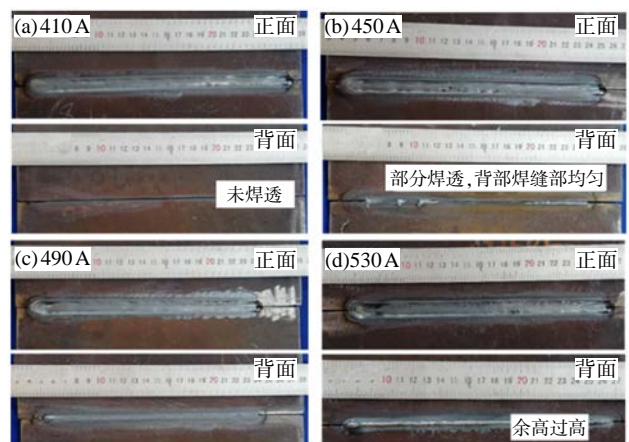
不同焊接电流下 K-TIG 焊缝表面成型
